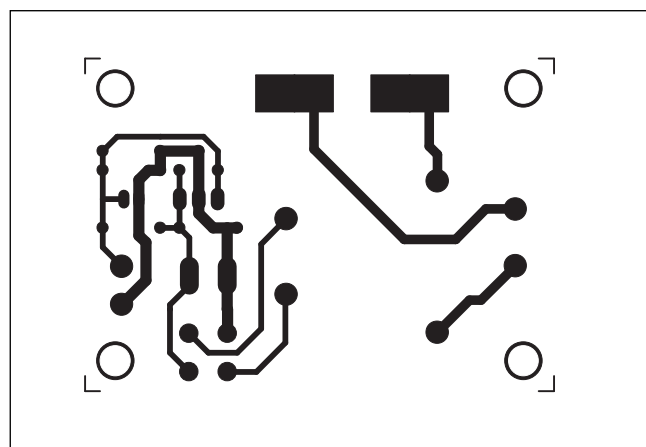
Obrazec desky spojů modulu (A99868)
